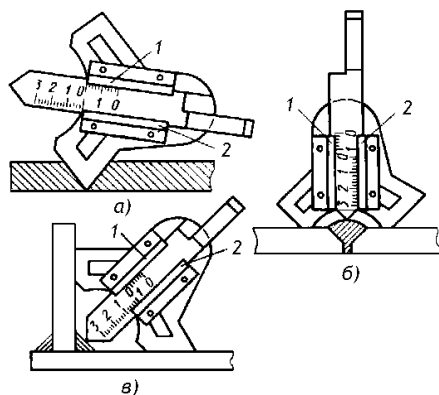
Универсальный измеритель швов, где а – проверка угла скоса кромок, б – проверка величины превышения усиления шва, в – проверка высоты углового шва; 1 – шкала выпуклости стыкового шва. 2 – шкала высоты углового шва
